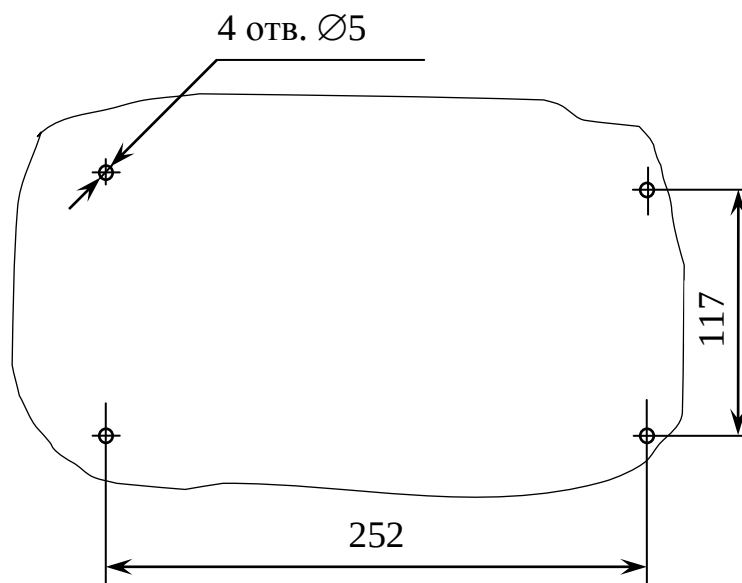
Разметка отверстий для крепления блока преобразовательного настенного исполнения на вертикальной поверхности
